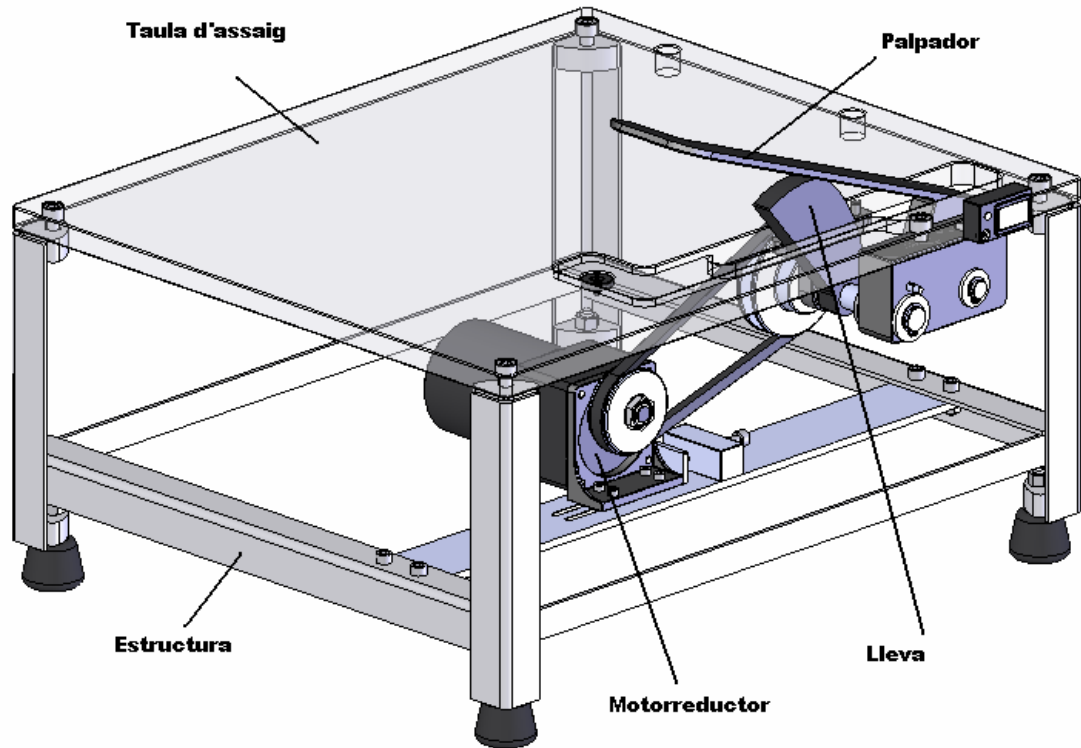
Vista general de la màquina d'assaig i designació principals components.
